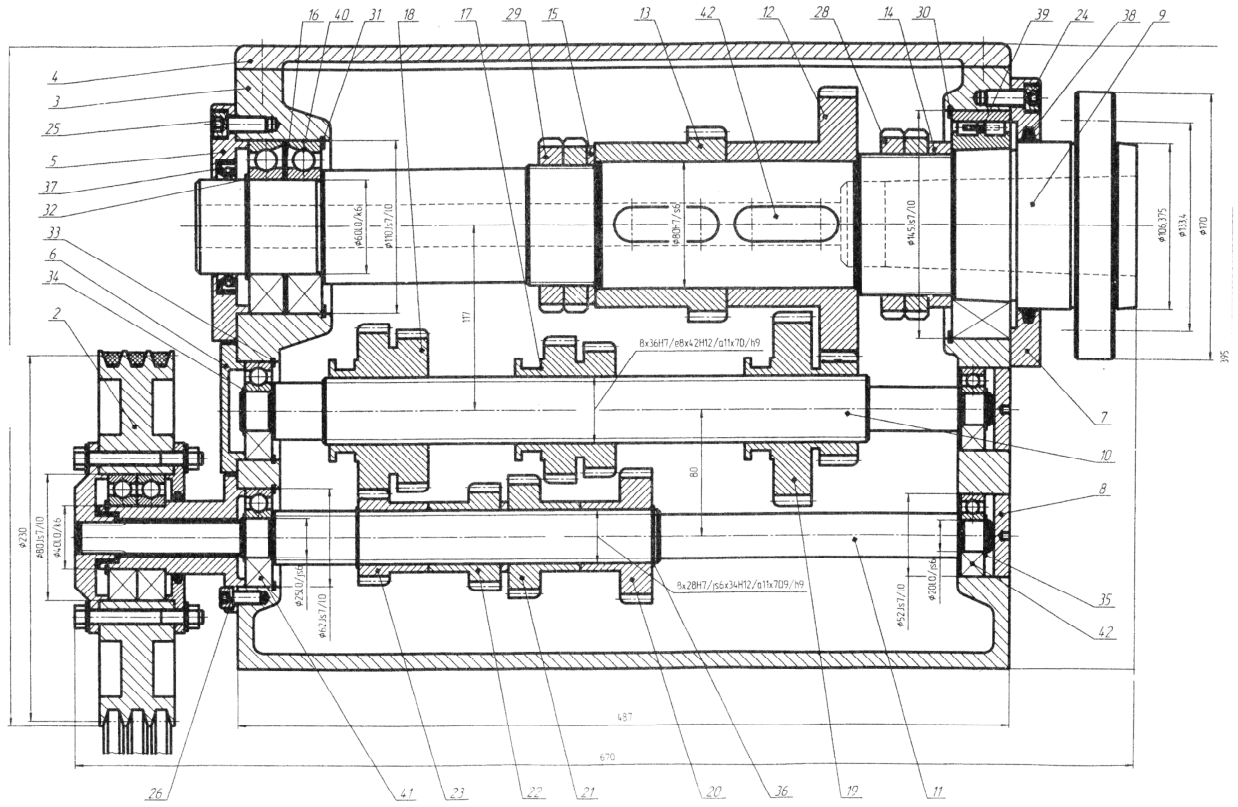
Приклад креслення розгортки коробки швидкостей токарного верстата
